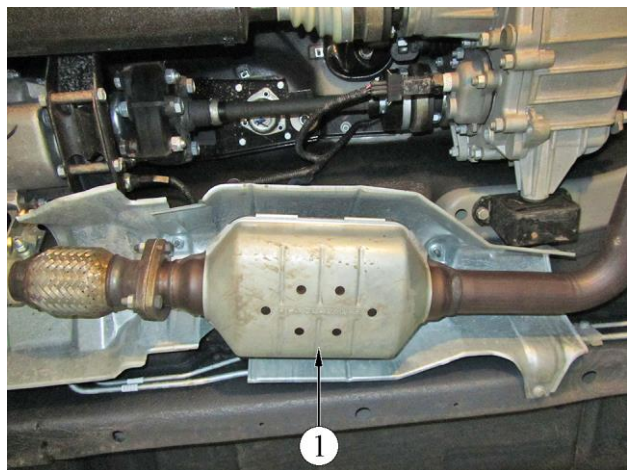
Расположение каталитического нейтрализатора (вид снизу): 1 - каталитический нейтрализатор
